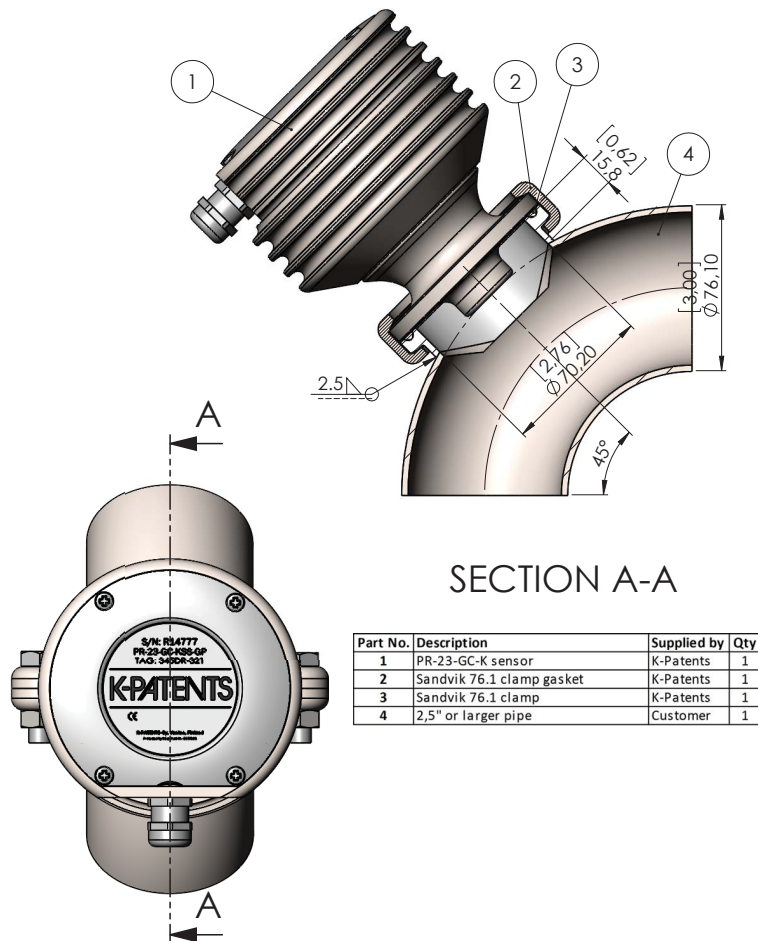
Montaje del sensor en una tubería de 2 1/2" o más
